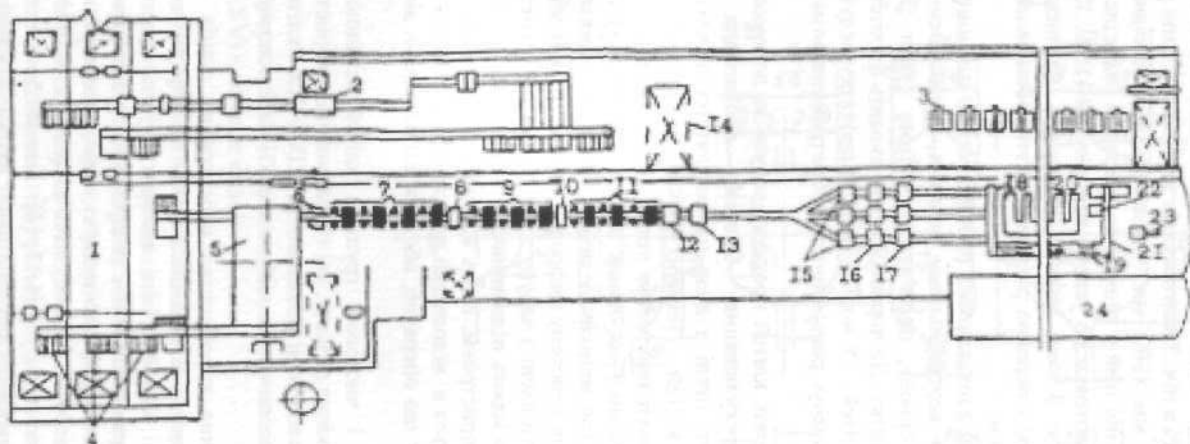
Схема розташування устаткування дрібносортового стану 250: 1 - склад заготівлі; 2 - лінія дефектоскопії; 3 - обдирання-шліфувальні верстати; 4 - завантажувальні ґрати; 5 - нагрівальна піч; 6 - пристрій для гідросбива окалини; 7 - чорнова група клітей; 8,10,12,13 - кривошипні ножиці; 9 - проміжна група клітей; 11 - чистова група; 14 - підйомний кран; 15 - трайбапарат; 16 - моталки; 17 - бунтовязальні машини; 18 - рольганг; 19 - транспортер бунтів з крокуючими колосниками; 20 - пакуєчий пристрій; 21 - рольганг; 22 - бунтознімальне пристрій; 23 - установка для розмотування і правки бунтового прокату; 24 - термічне відділення
